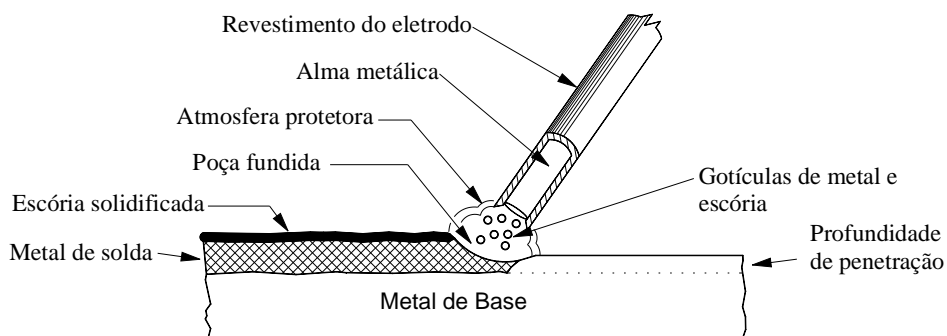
Processo de soldagem com Eletrodo Revestido.
